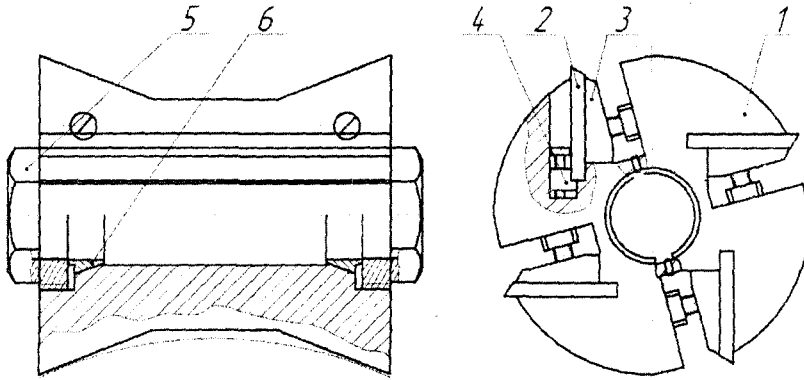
Конструкция фасонной фрезы, обеспечивающая точное центрирование на шпинделе станка
